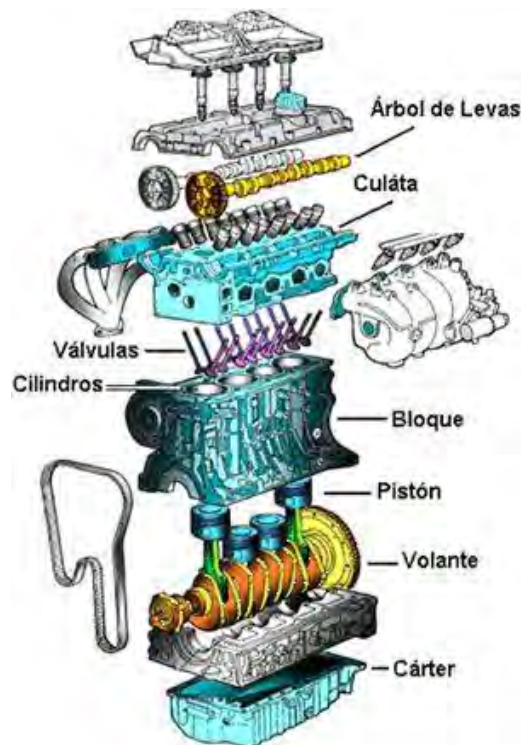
1 Partes del motor de explosión de 4 cilindros.
